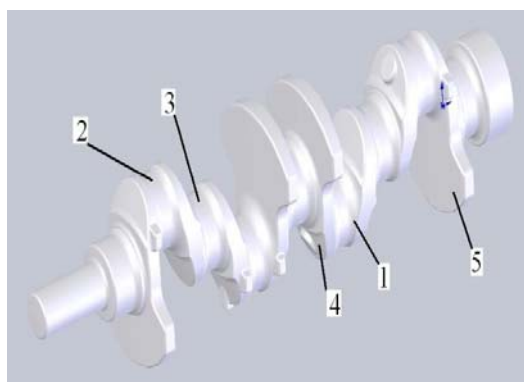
3D модель отливки «Вал коленчатый»
